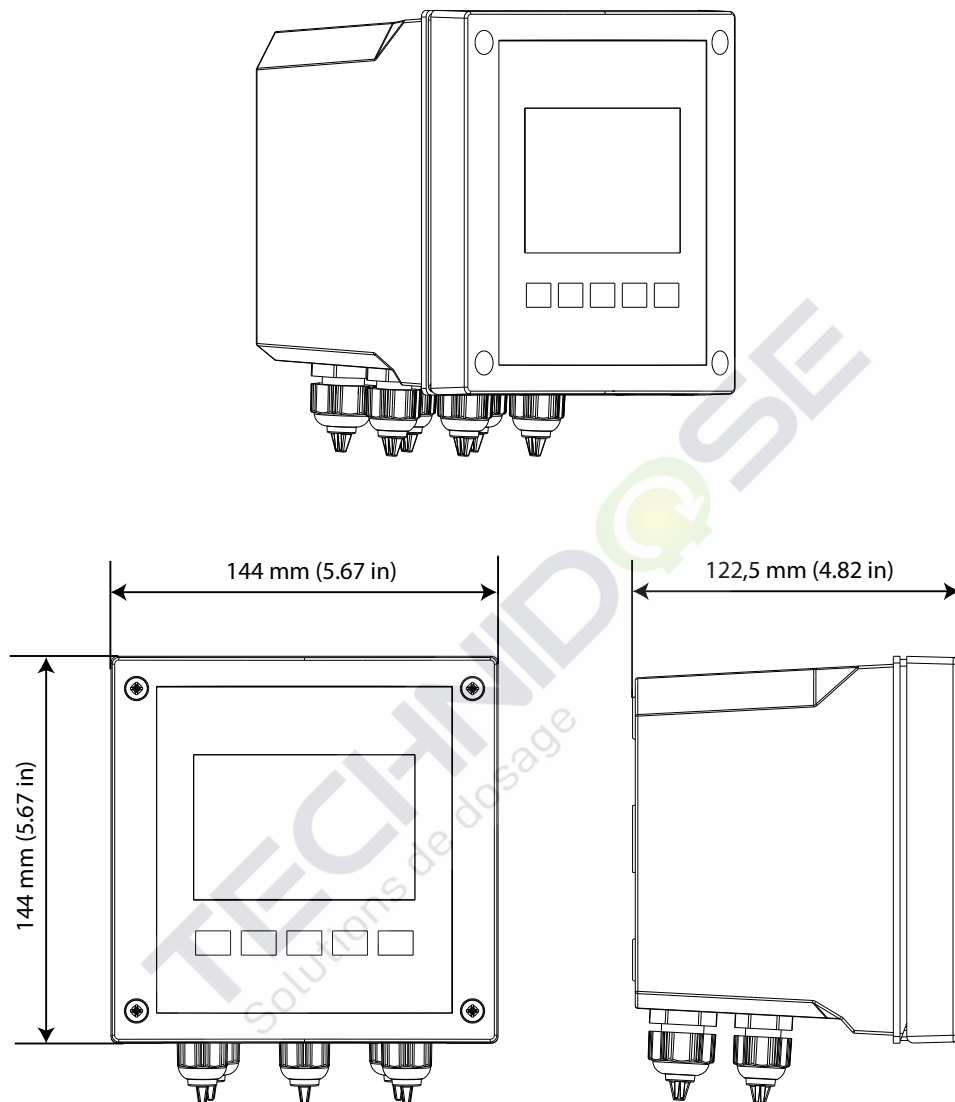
Dimensions et encombrement du dispositif à montage mural
